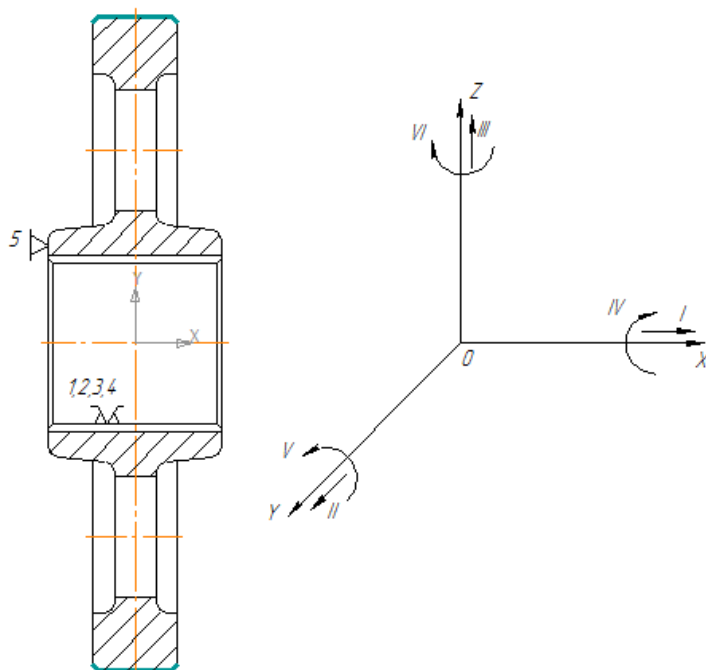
Схема базування заготовки на шліцьову оправку
